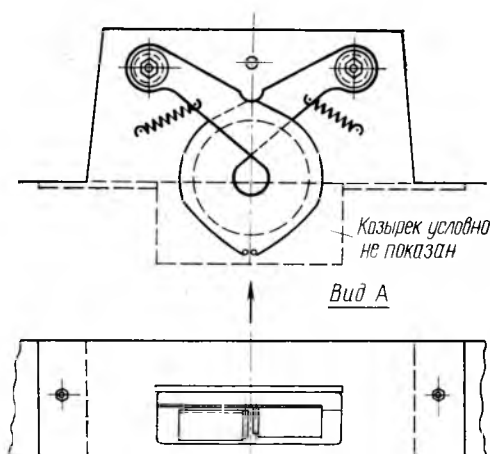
Ограждение к фрезерному станку для пазовальных операций
